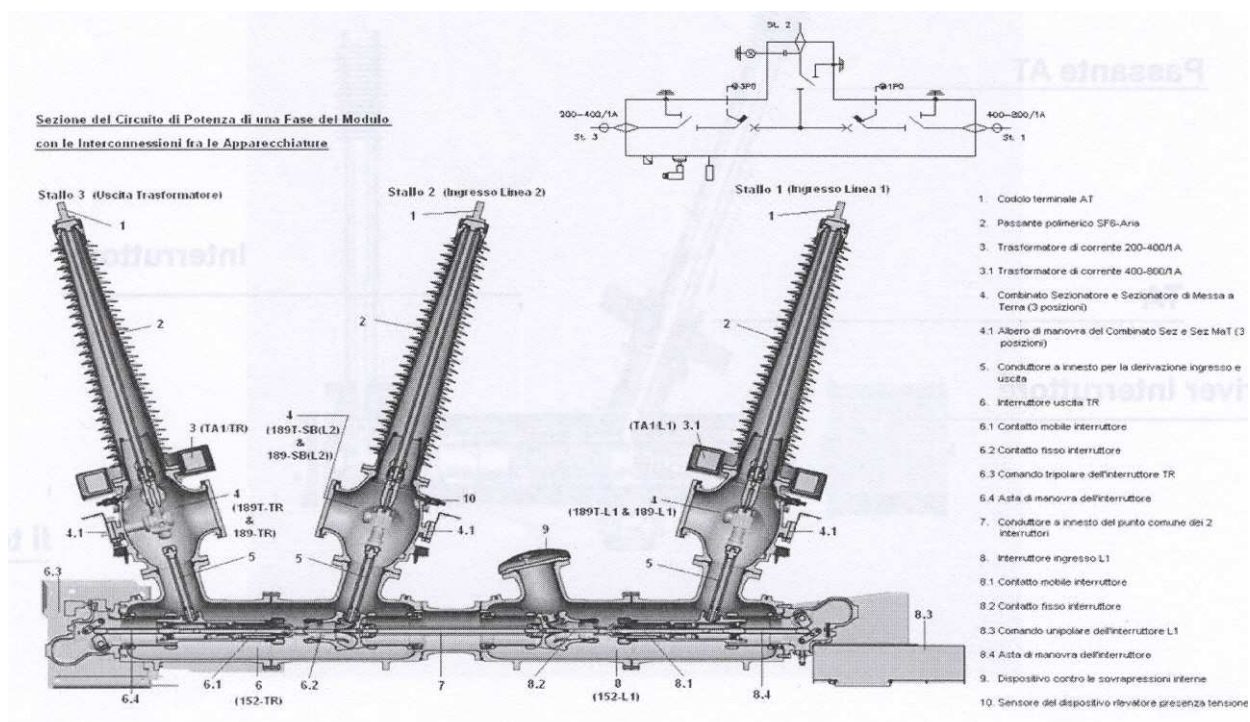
Modulo ibrido “Y2” della sezione AT (sezione interna)
